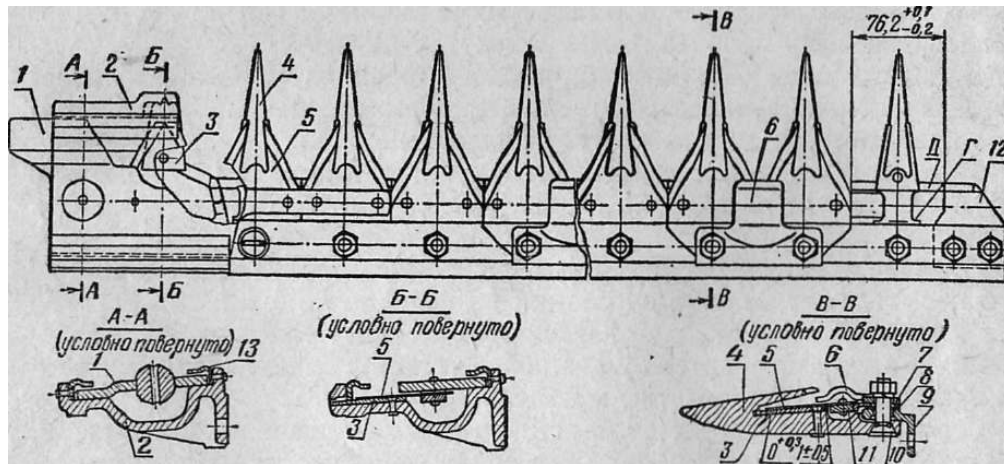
Режущий аппарат: Г — буртик; Д — ус; 1 — головка ножа; 2 — направляющий кронштейн; 3 — вкладыш; 4 — палец; 5 — сегмент ножа; 6 — прижим ножа; 7 — пластина трения; 8 — регулировочная прокладка; 9 — пальцевый брус; 10 — болт; И — спинка ножа; 12 — упорная пластина; 13 — сменная пластина трения.
